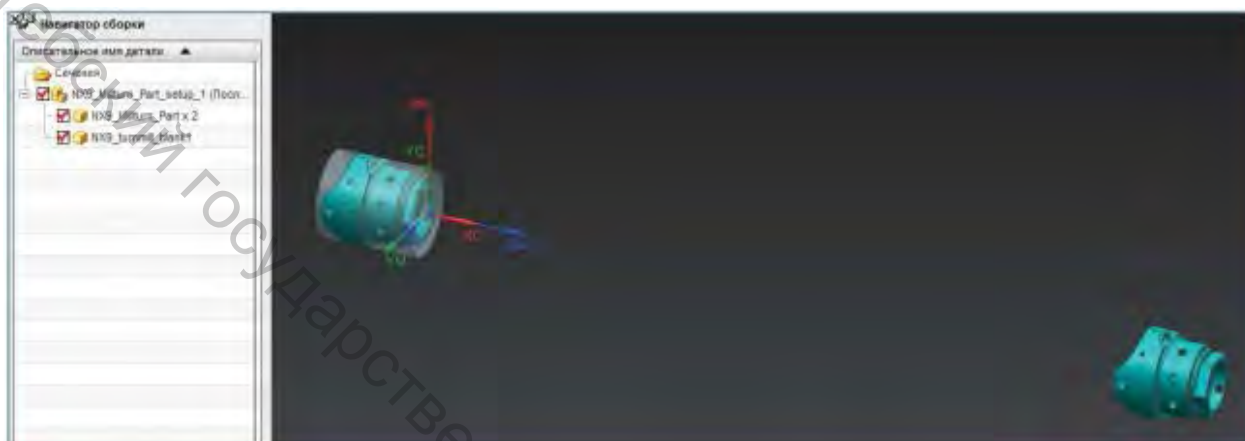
Создание деталей для токарно-фрезерной обработки за два станова
